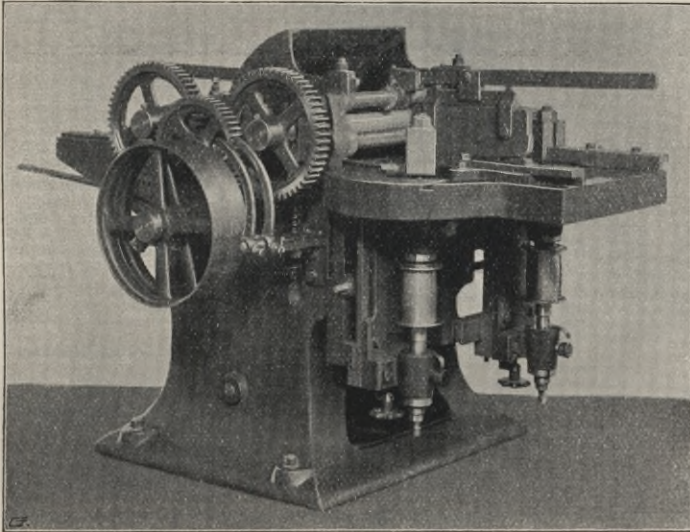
Walzenhobelmaschine mit drei Messerwellen.
